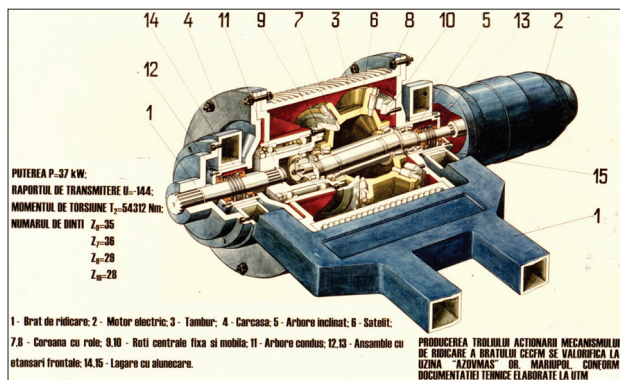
Mecanism de acționare a tamburului Complexului Robotizat cu reductor precesional 2K-H
